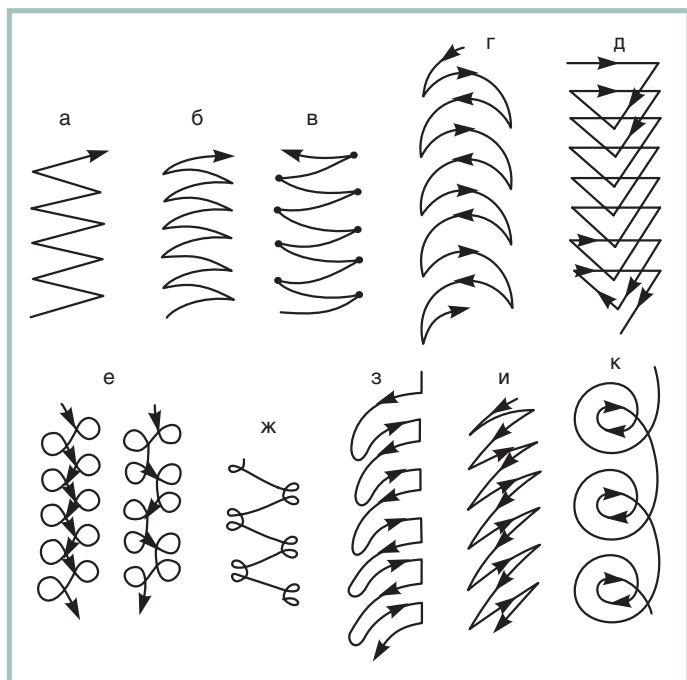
Основные виды траекторий поперечных колебаний конца электрода при ручной дуговой сварке
